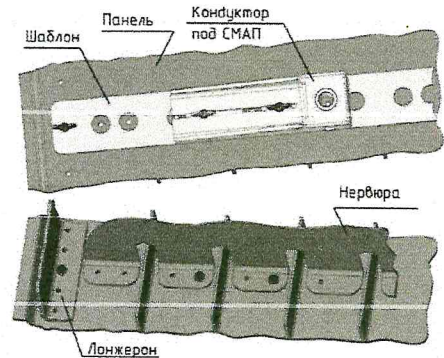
Кондуктор для сверления отверстий по нервюрам
